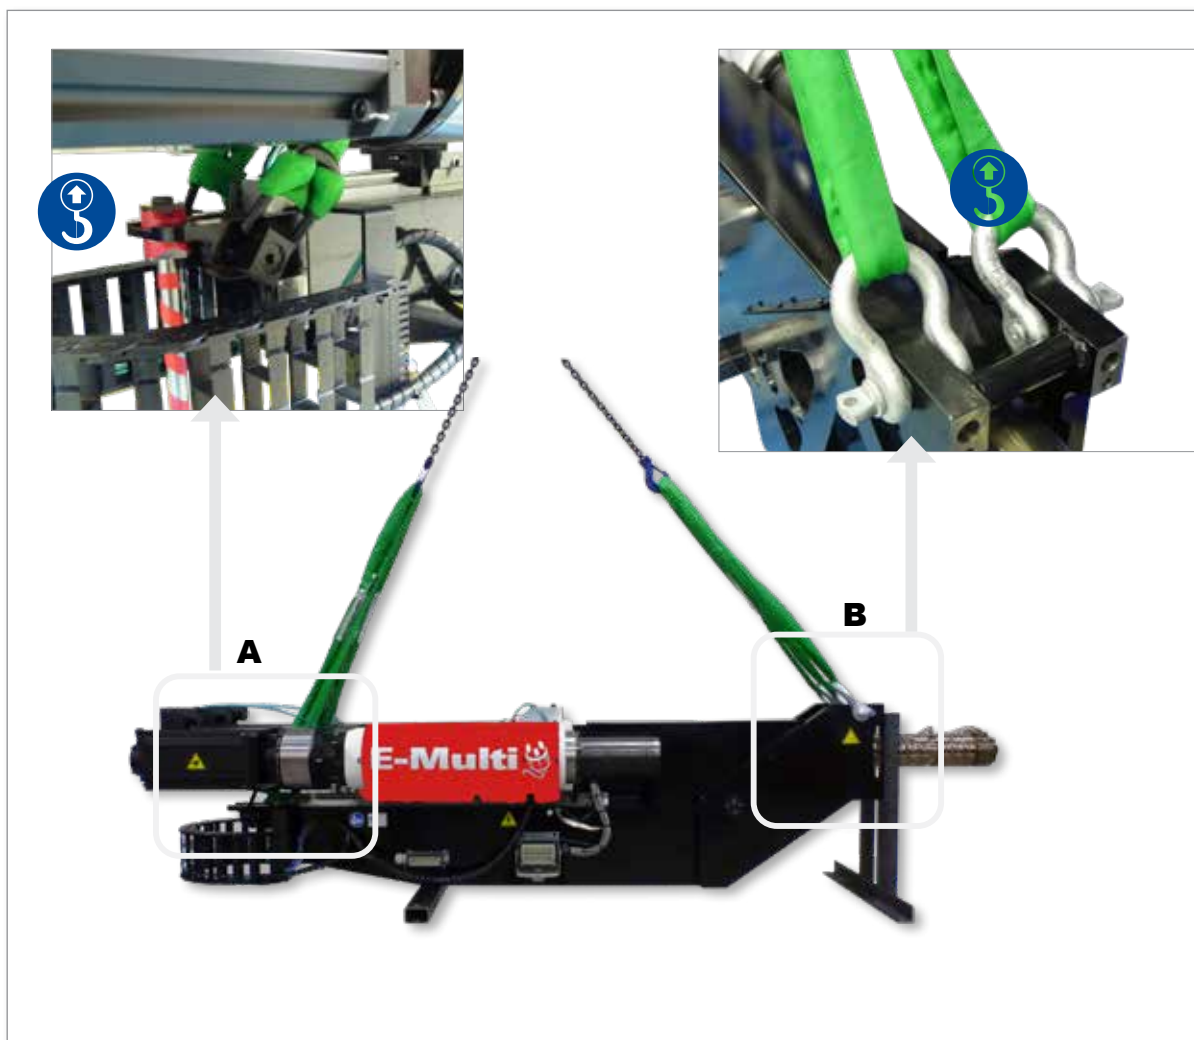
Collegamenti di sollevamento orizzontale EM4
